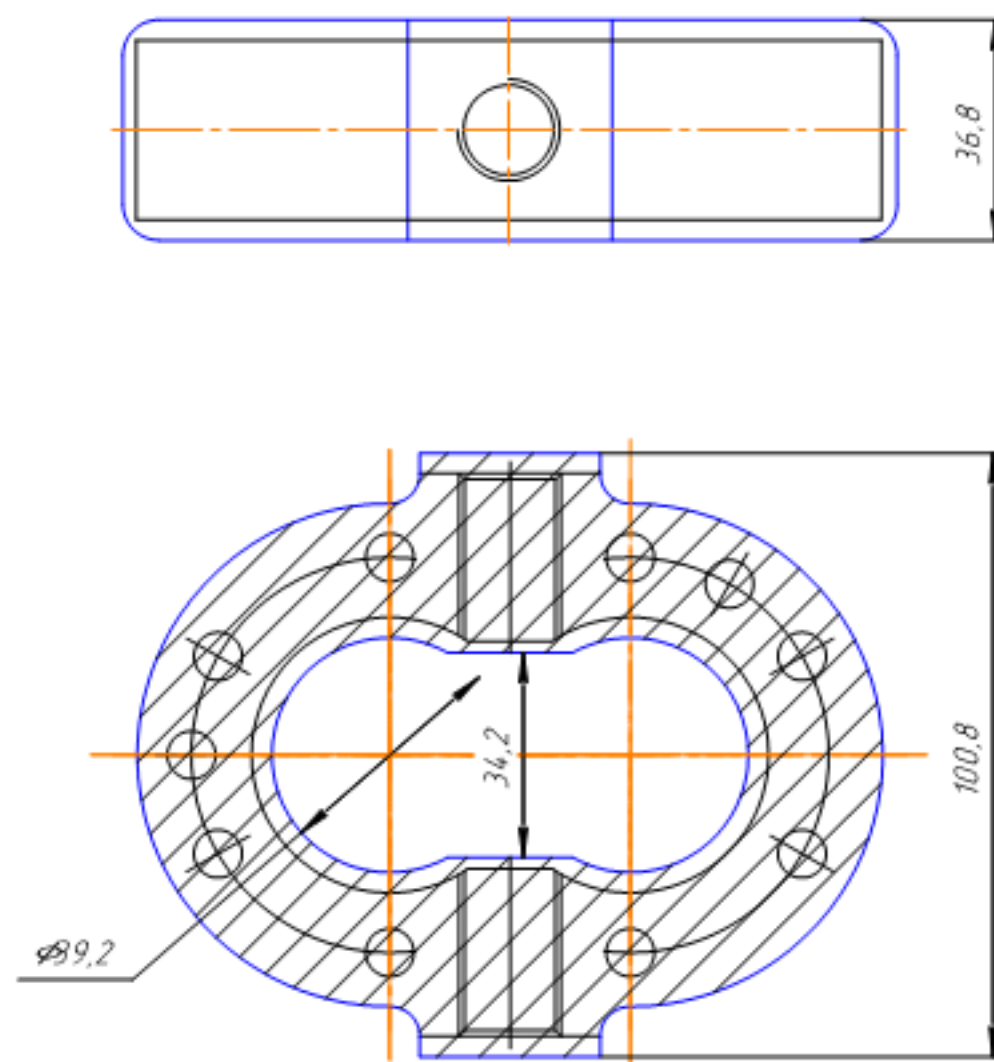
Ескіз заготовки при литті в оболонкові форми
